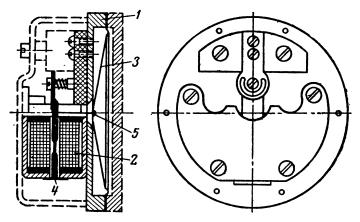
Устройство громкоговорителя с капсюлем ДЭМ. I—корпус; 2—катушка, 3— диффузор; 4—якорь; 5— шпилька.
